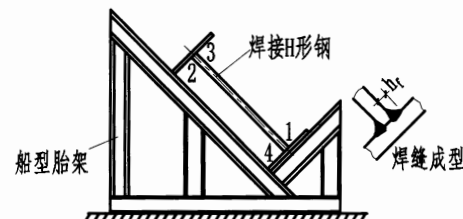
H形钢腹板与翼缘板为角焊缝的焊接
